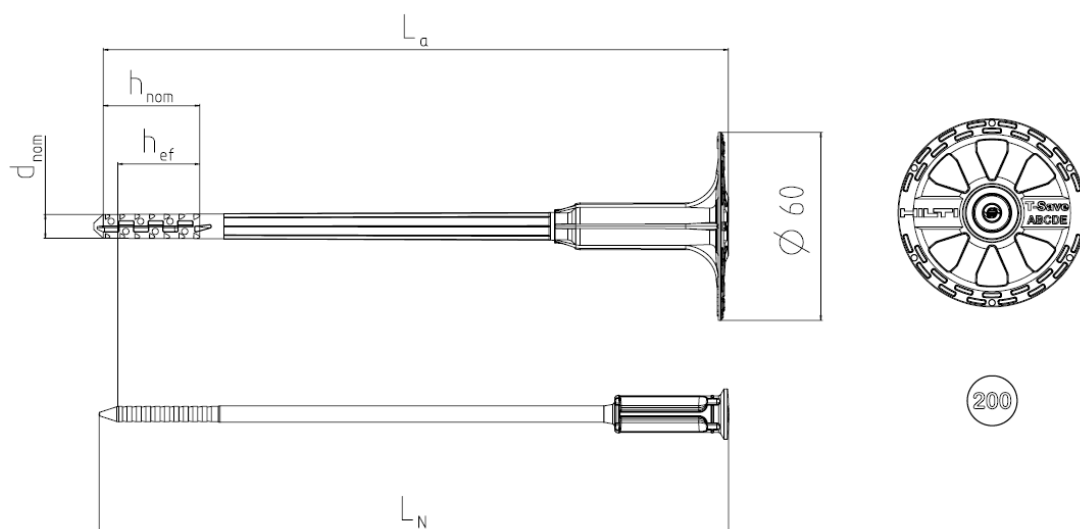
T-Save HTS-P - manchon assemblé, rosace (rondelle ou plaque) et fût en plastique
